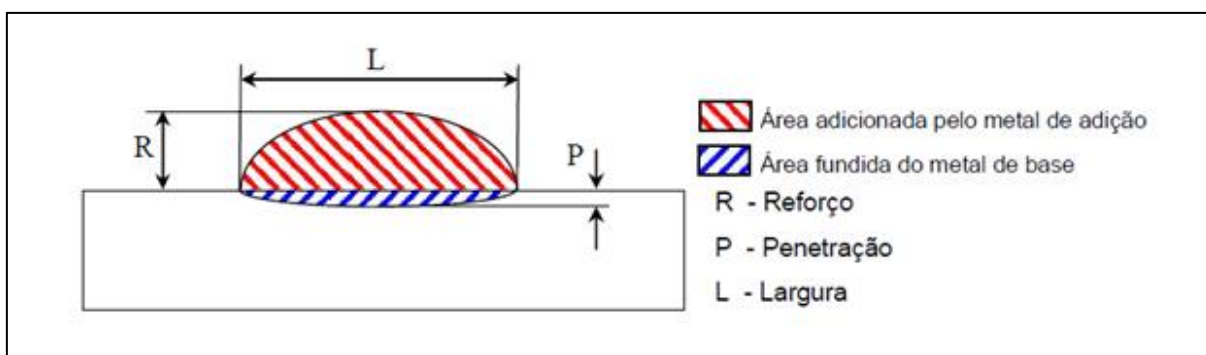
Desenho esquemático das características geométricas e diluição para um cordão de solda.
